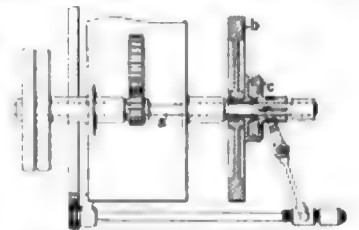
Hilfsumsteuerung für Werkzeugmaschinen.
